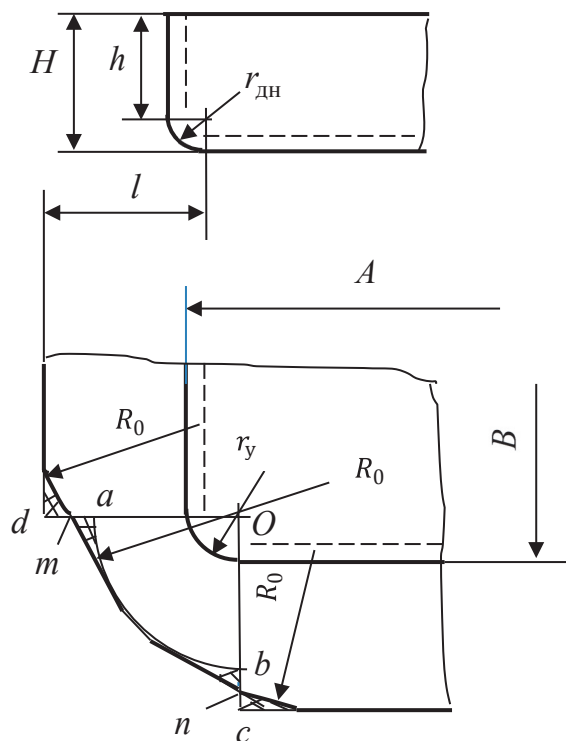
Схема построения угловых участков заготовок для вытяжки низких коробчатых деталей
